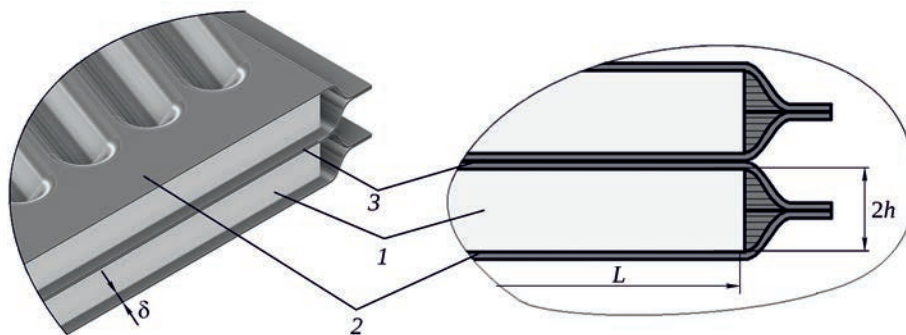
Технологические вставки для сварки конвертов и их геометрия:
